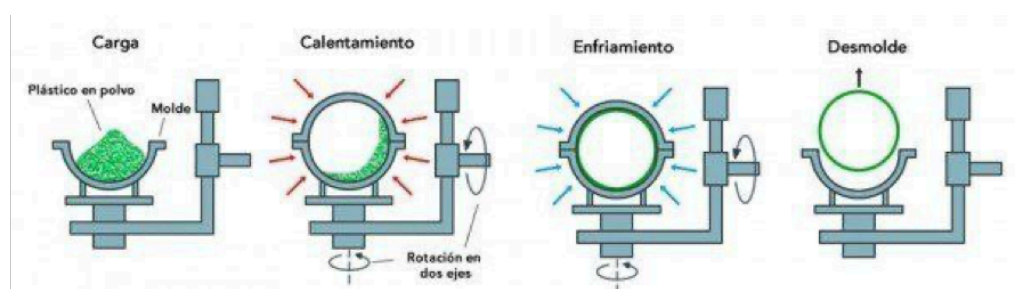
Proceso de moldeo rotacional o rotomoldeo [60].
